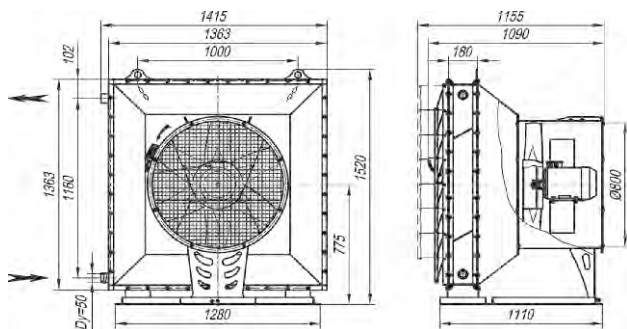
Габаритные и присоединительные размеры агрегата СТД-300 на базе водяного воздухонагревателя типа КСк.
